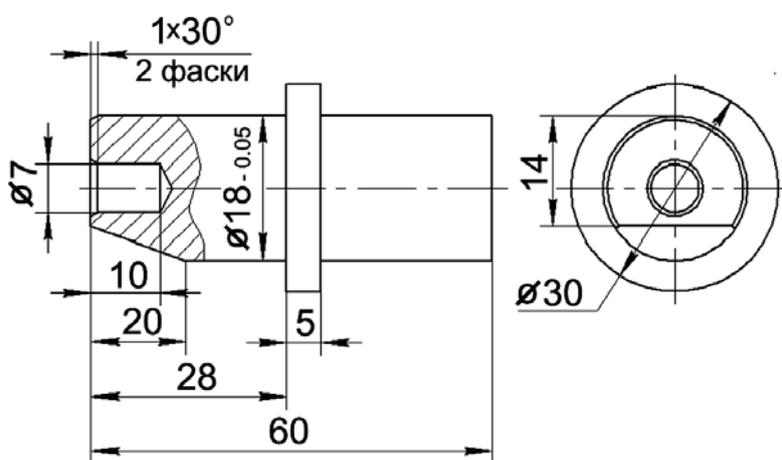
Приспособление для фиксации установочного штифта.
